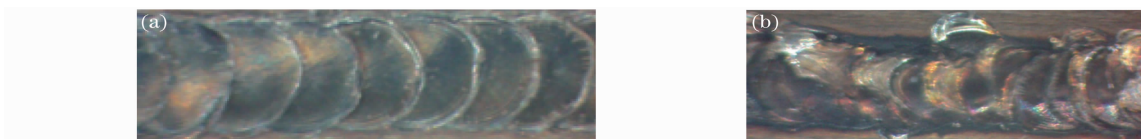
焊缝的典型表面形貌。(a)表面焊接质量较好试样,(b)表面已产生飞溅试样
